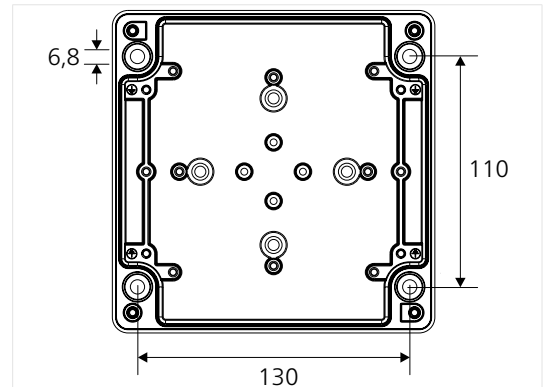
Abmessungen für Montagelöcher (Angaben in mm)
